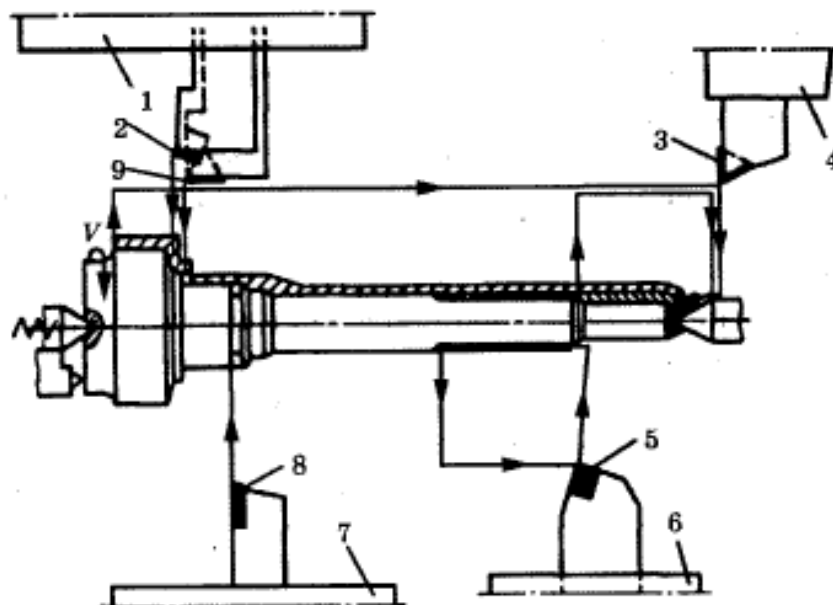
Схема обточування валу на багаторізцевому верстаті
